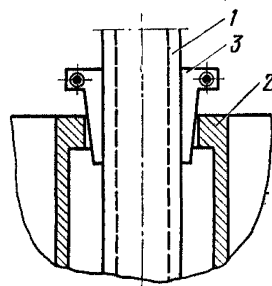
Устранение зазоров между валом и ступицей ротора в РВП ТКЗ первых допусков.
